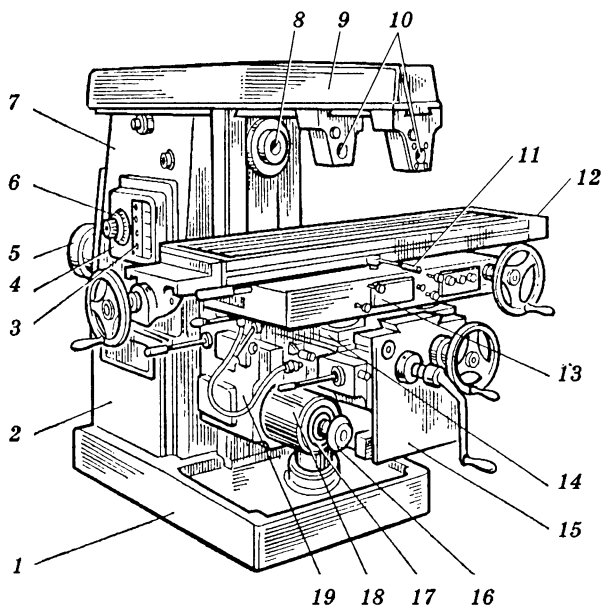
Горизонтальный консольно-фрезерный станок 6P18Г6: 1 — плита; 2 — станина; 3 — кнопочная станция; 4 — коробка переключения скоростей; 5 — электродвигатель; 6, 17 — лимбы; 7 — участок станины; 8 — шпиндель; 9 — хобот; 10 — подвески (серьги); 11 — рукоятка; 12 — стол; 13 — поворотная часть; 14 — каретка; 15 — консоль; 16 — маховичок; 18 — коробка переключения подач; 19 — коробка подач
